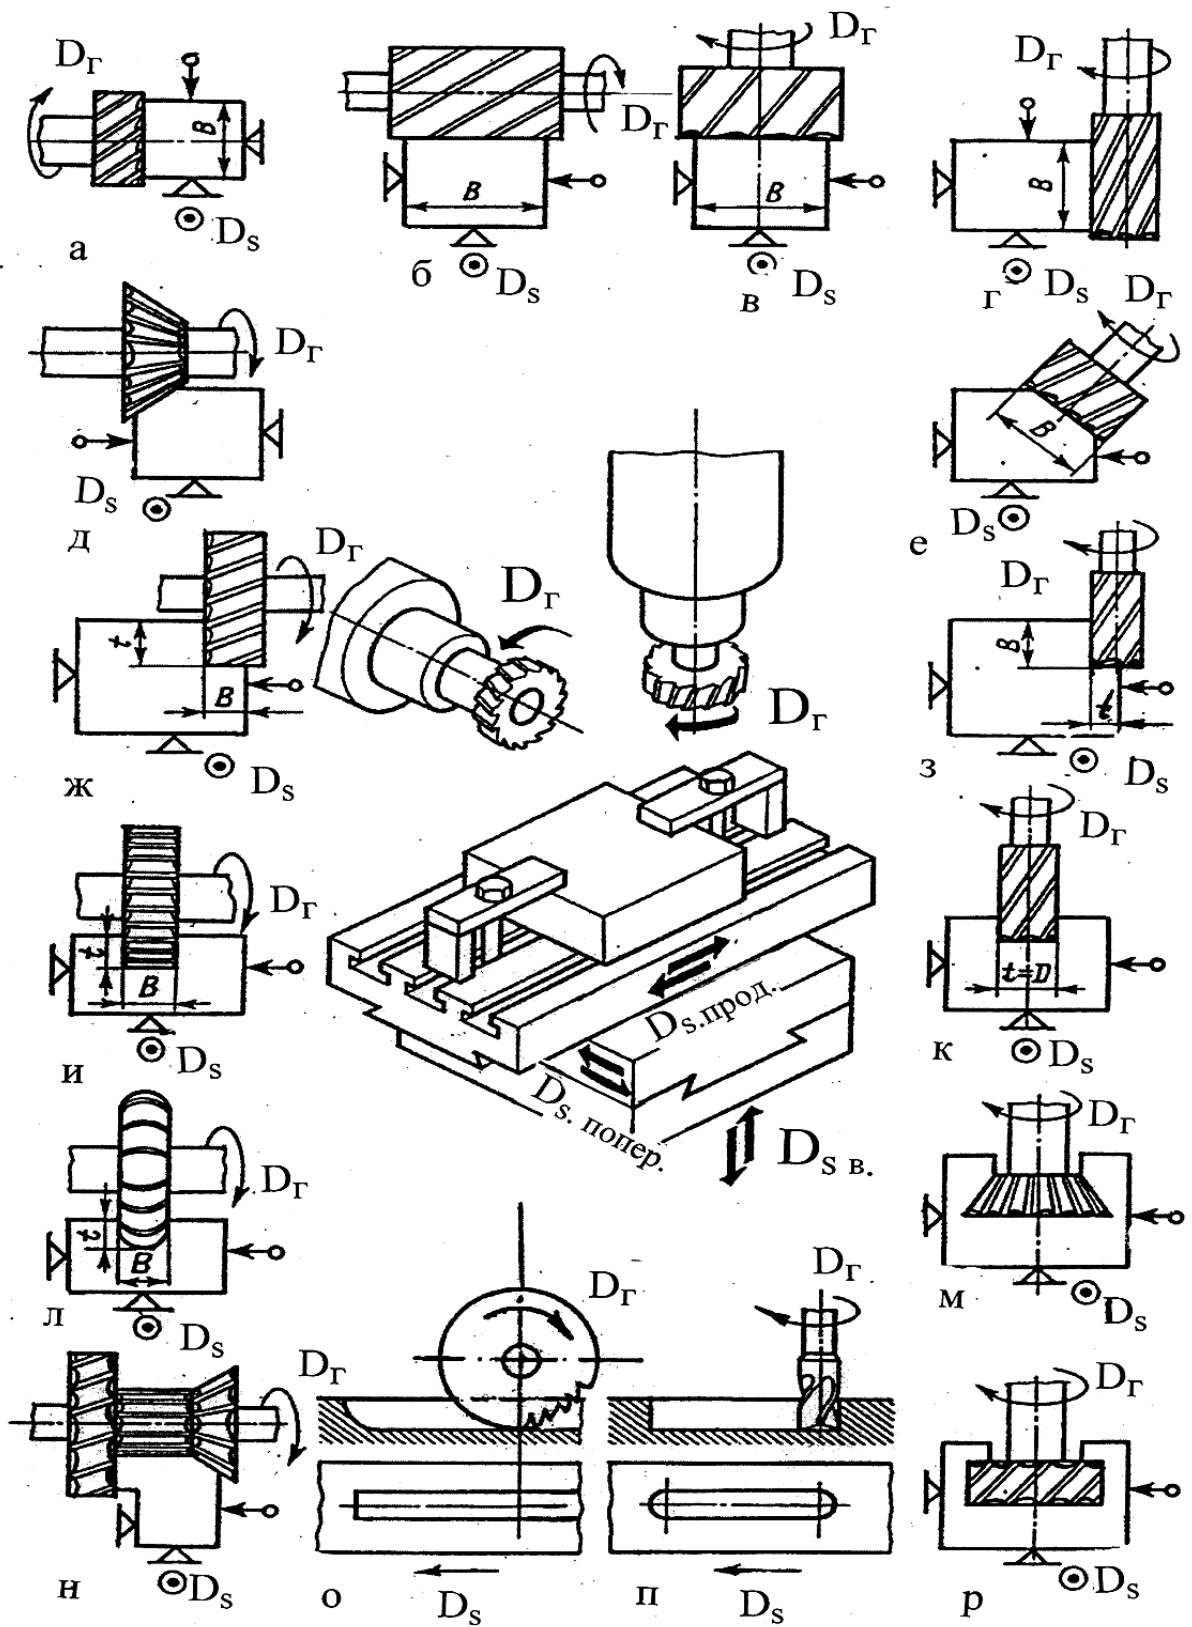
Схемы фрезерования поверхностей обрабатываемых заготовок
